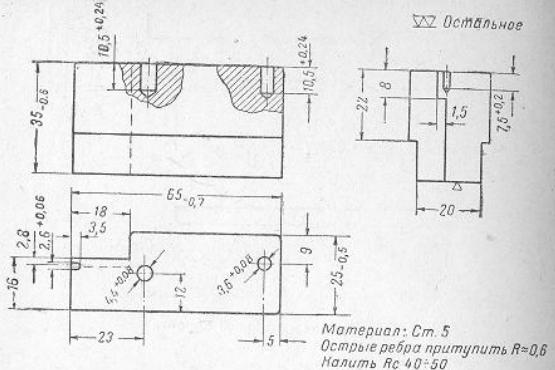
Подставка для расклепки головок осей спускового крючка, курка и казенника
